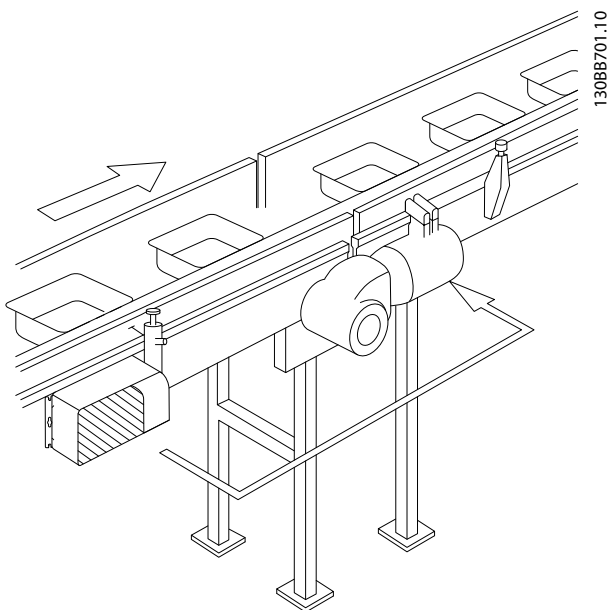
FCD 302 independente montado com suportes de montagem
